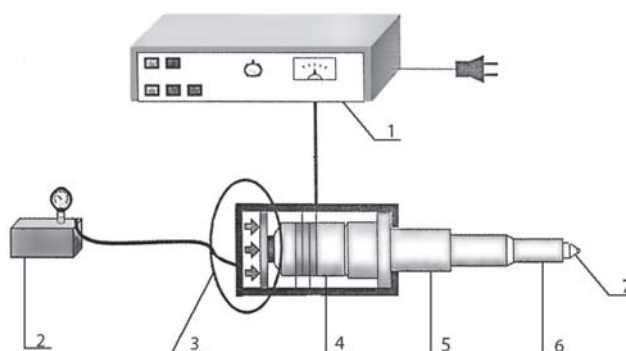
Схема установки для ультразвуковой упрочняющей обработки с пьезокерамическим преобразователем:
